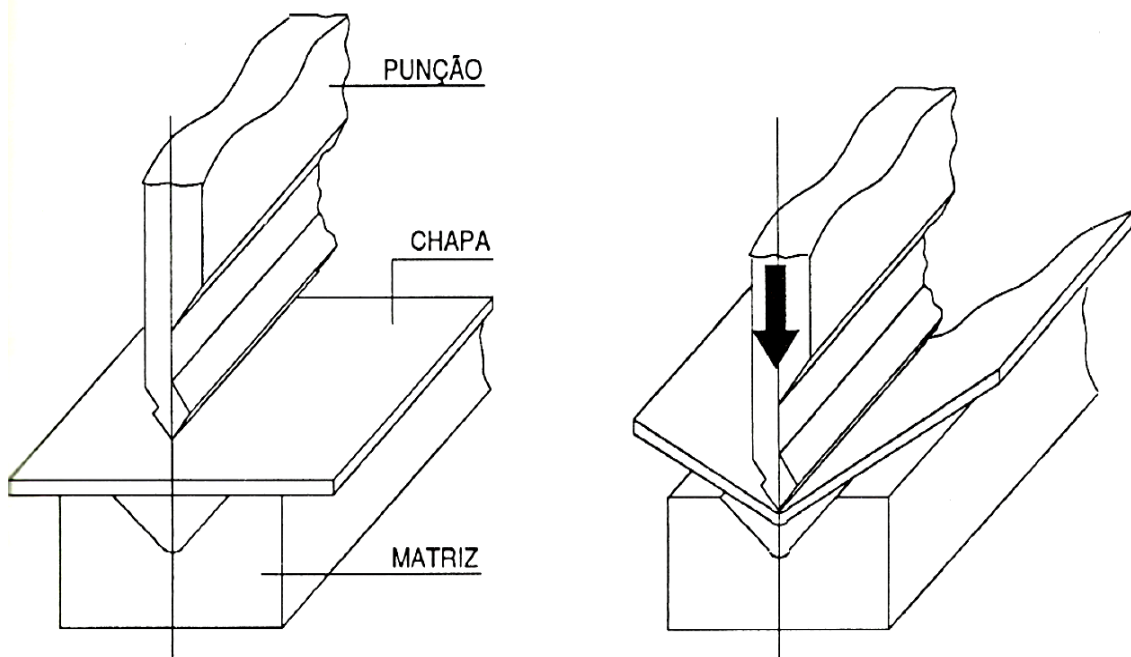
Posições relativas da chapa a quinar e das ferramentas antes e durante a quinagem
